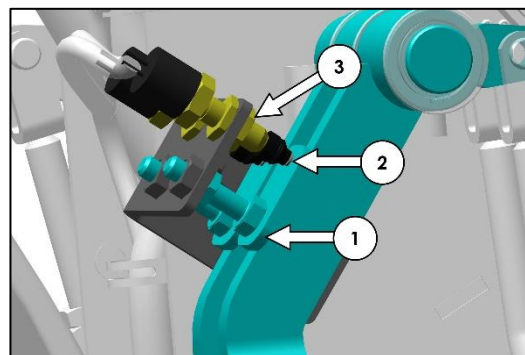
RÉGLAGE DES CONTACTEURS DE FREIN
